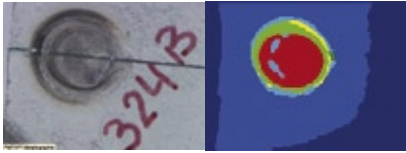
Schweißpunkt, links Realbild, rechts Thermogramm
